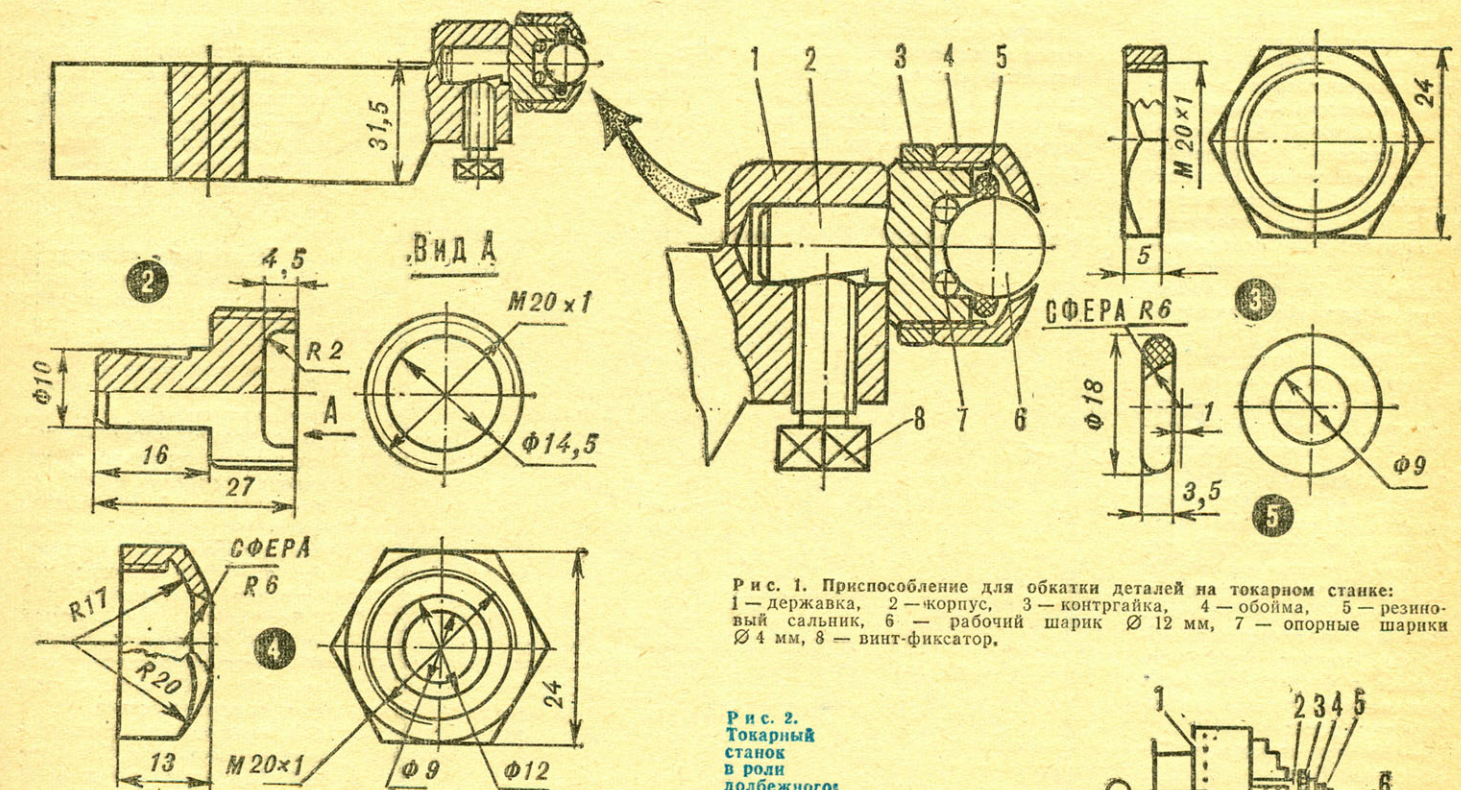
Приспособление для обкатки деталей на токарном станке: 1 — державка, 2 — корпус, 3 — контргайка, 4 — обойма, 5 — резиновый сальник, 6 — рабочий шарик $\varnothing 12$ мм, 7 — опорные шарики $\varnothing 4$ мм, 8 — винт-фиксатор.
